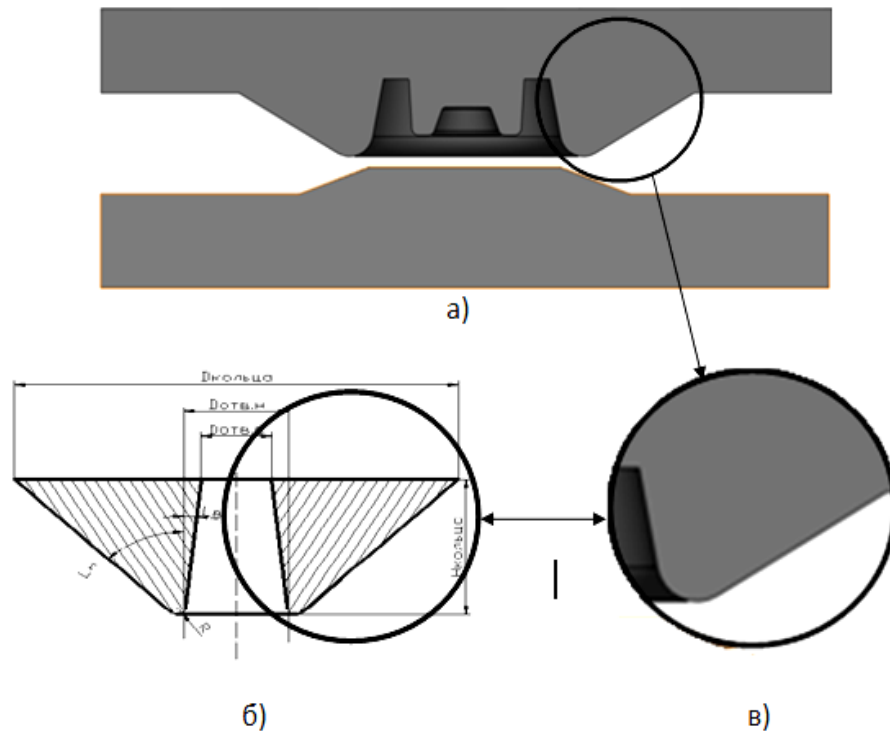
Переріз кільцевого конусного інструменту складної форми:
